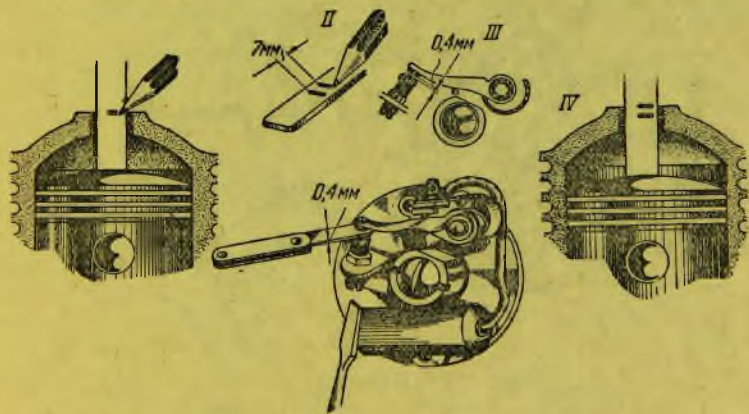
Регулировка зазора между контактами прерывателя и установка момента зажигания
